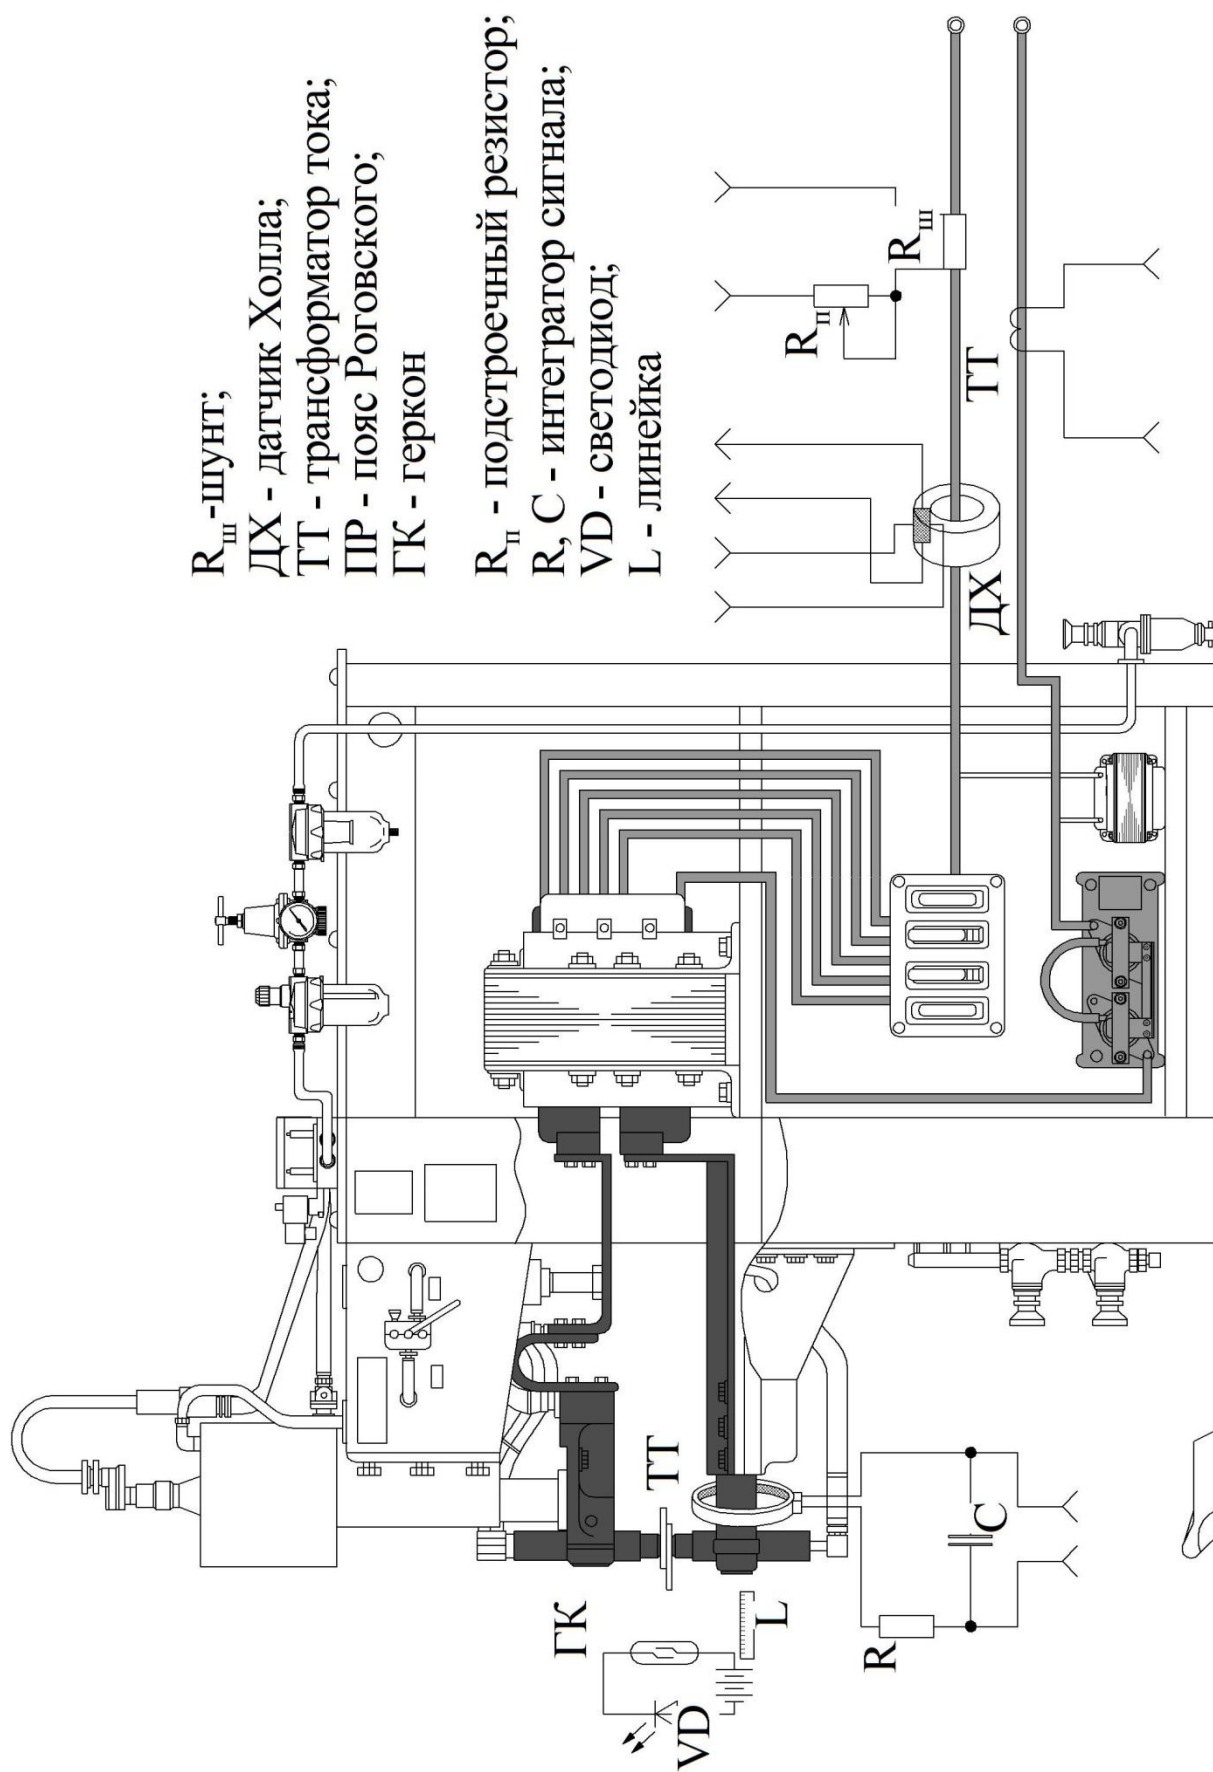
Измерение тока на машинах контактной сварки
